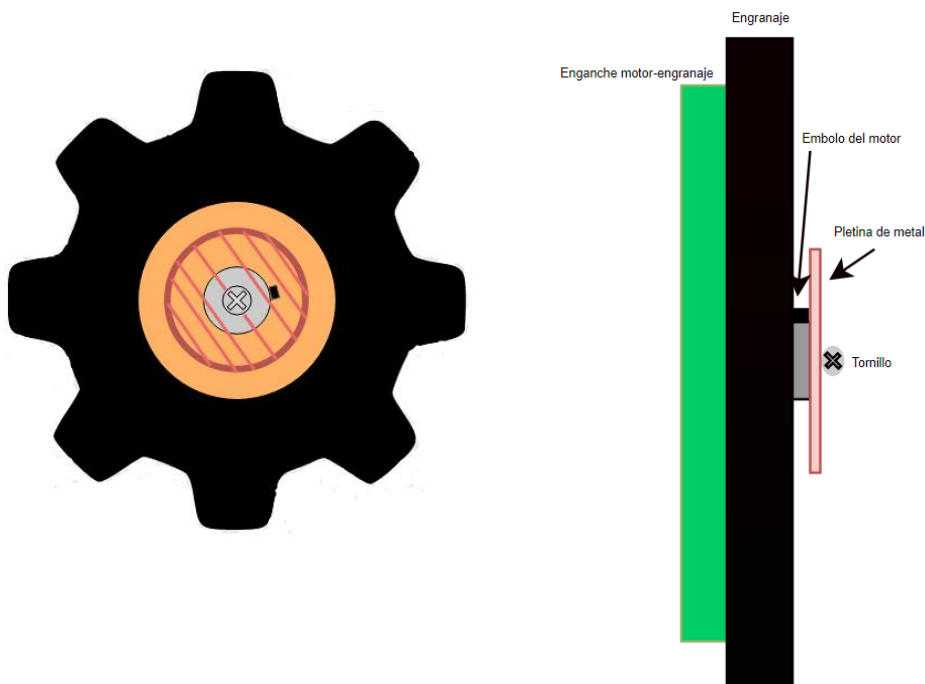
Partes implicadas en sujetar el engranaje del motor, vista al alza (izquierda) y vista de perfil (derecha).
